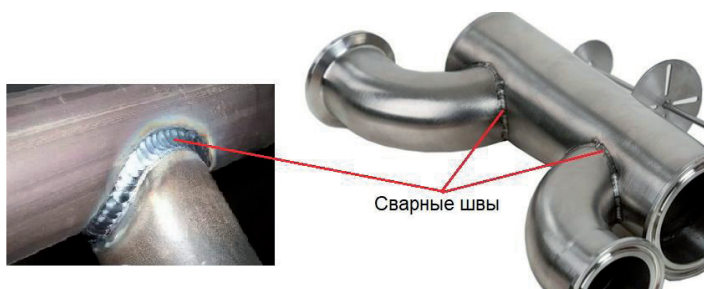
Сварные швы, выполняемые по линии пересечения поверхностей соединяемых деталей
